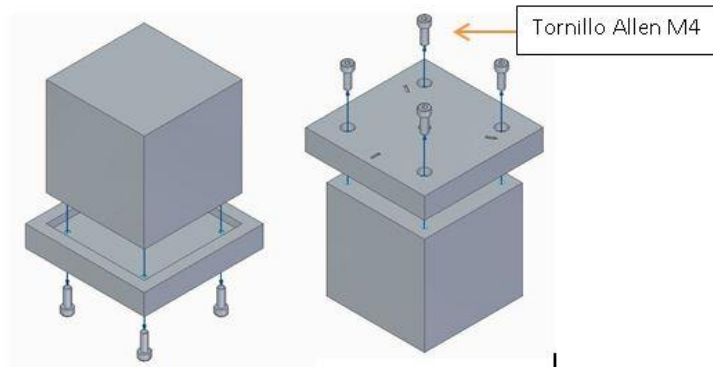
Proceso de montaje de la pieza de trabajo sobre la placa brida. Posición de sus componentes.
